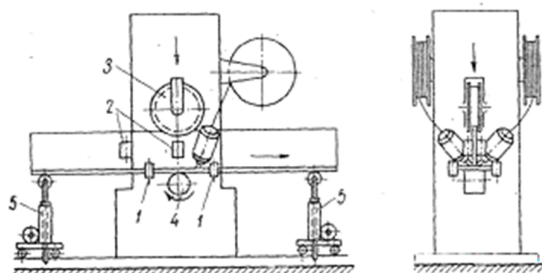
Принципова схема верстата «СТС» для зварювання балок таврового профілю
